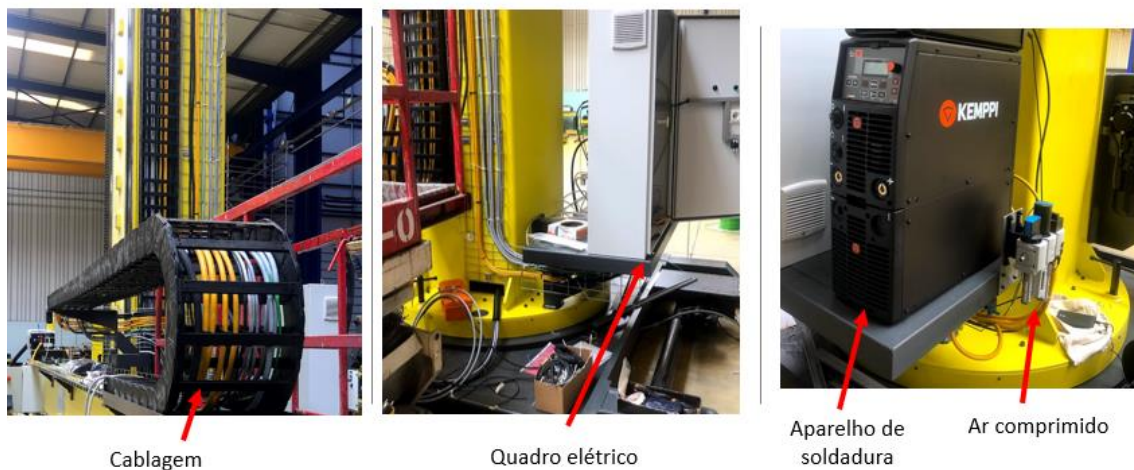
Cablagem, ligações elétricas, ar comprimido e aparelho de soldadura
